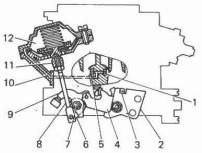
Esquema del mando de las mariposas del gas del carburador 2107-1107010:
